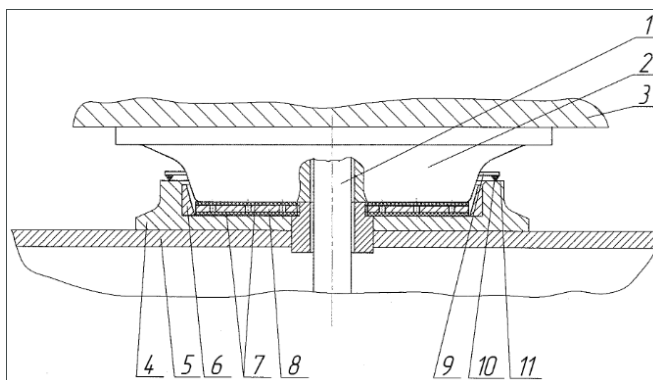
Пятниковый узел конструкции АО «ВНИКТИ»:
